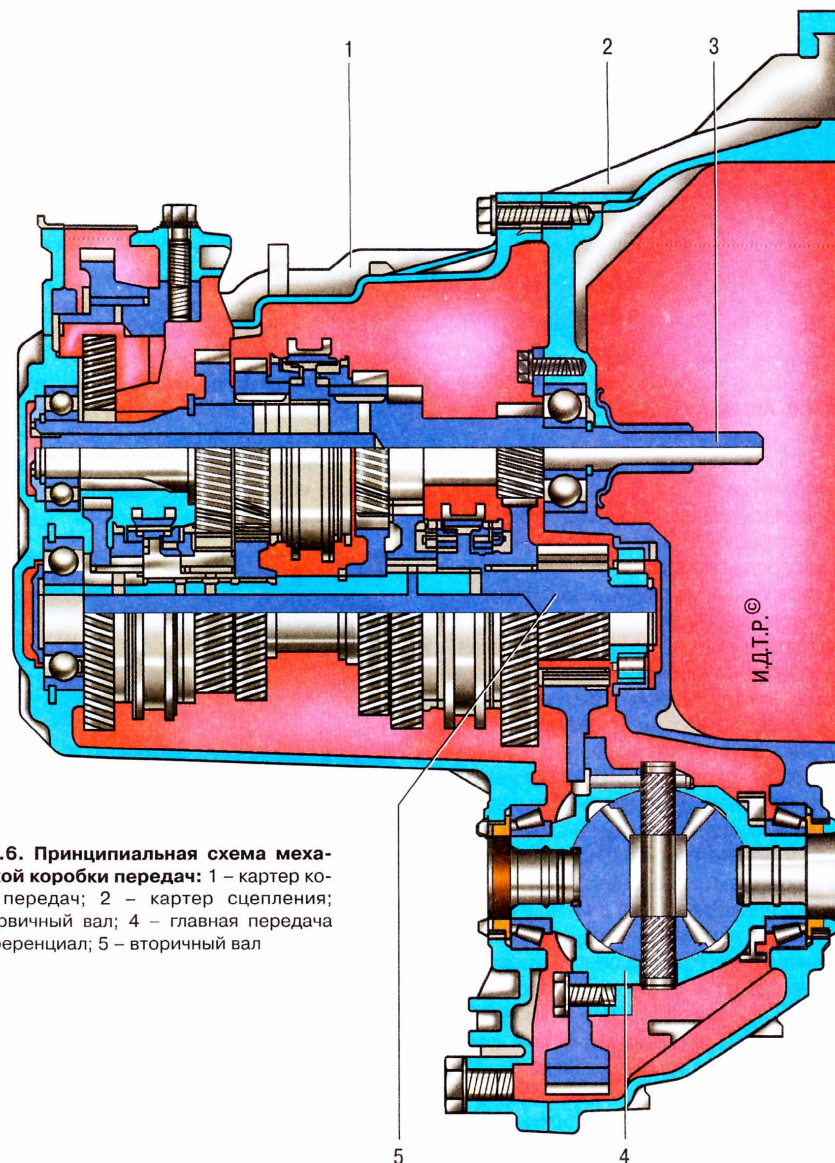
Принципиальная схема механической коробки передач: 1 — картер коробки передач; 2 — картер сцепления; 3 — первичный вал; 4 — главная передача и дифференциал; 5 — вторичный вал
